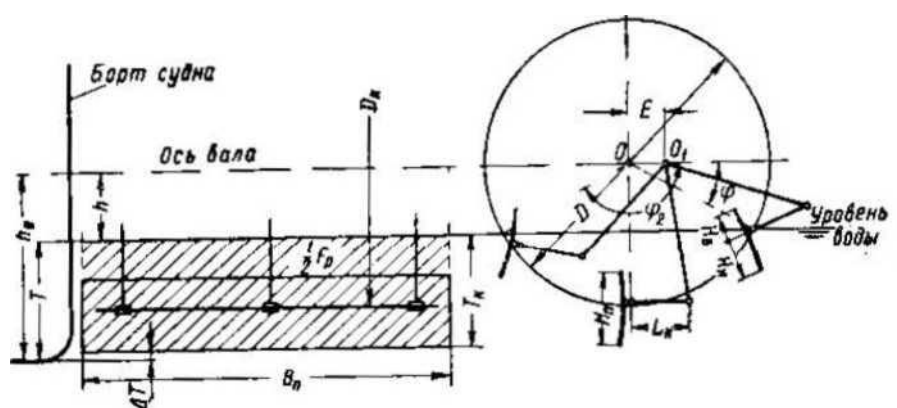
Конструктивные элементы гребного колеса с поворотными лопастями
